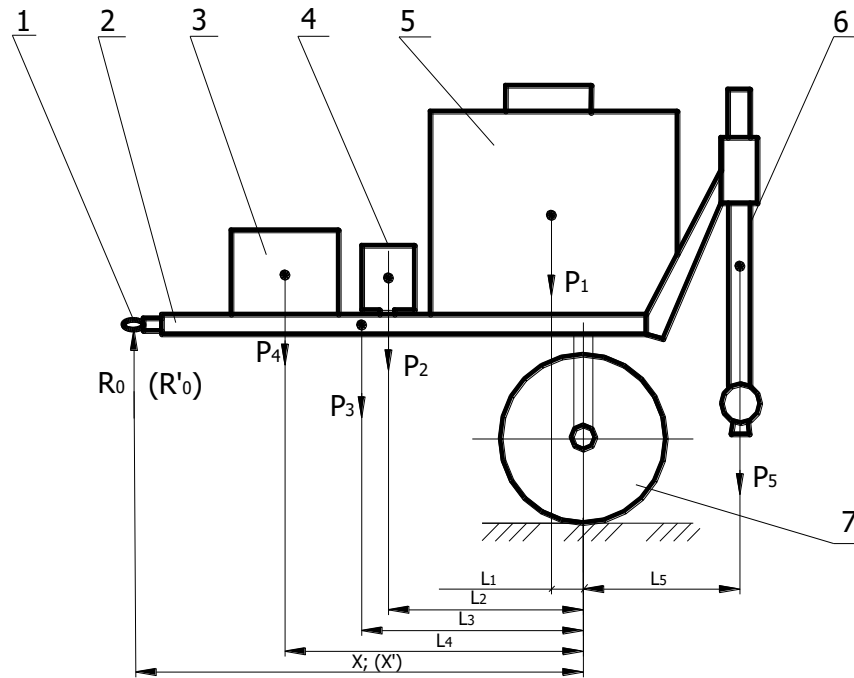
Розрахункова схема поздовжньої стійкості причіпного малогабаритного обприскувача: 1 – причіп; 2 – рама; 3 – насос; 4 – блок керуючий; 5 – бак з робочою рідиною; 6 – штанга в зборі; 7 – колесо опорне.
